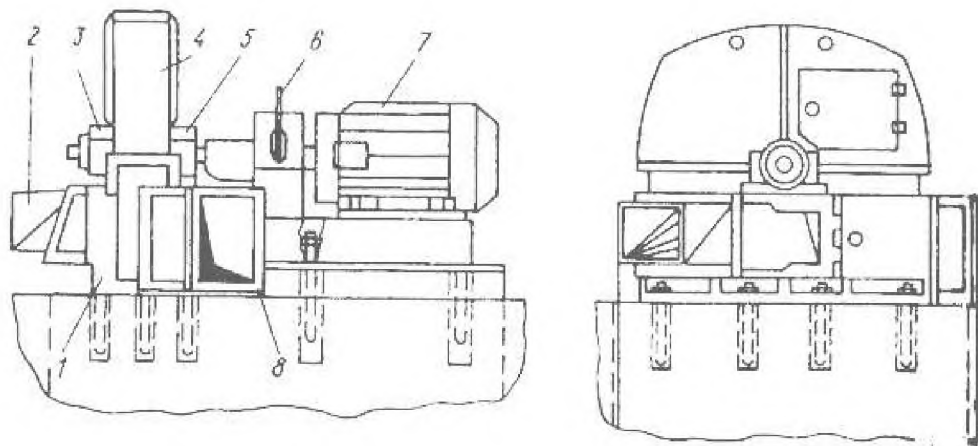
Рубальна машина МРЗ-40ГБ: 1 - станина; 2 - патрон подачі сировини; 3 - передня підшипникова опора; 4 - кожух ротора; 5 - задня підшипникова опора; 6 - рукоять гальма; 7 - електродвигун привода ротора; 8 - патрубків викиду стружки
